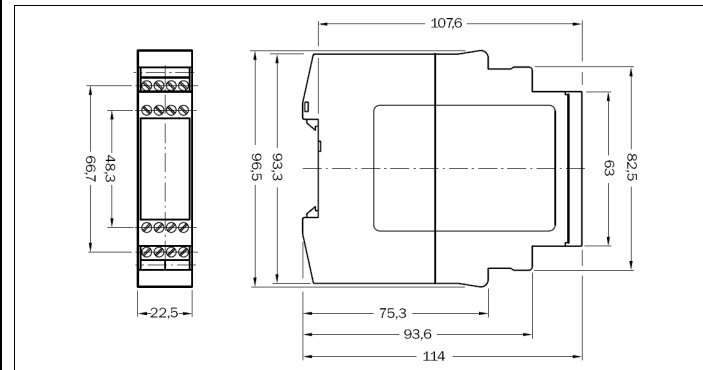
Maßbild UE42-2HD mit Schraubklemmen (mm)
